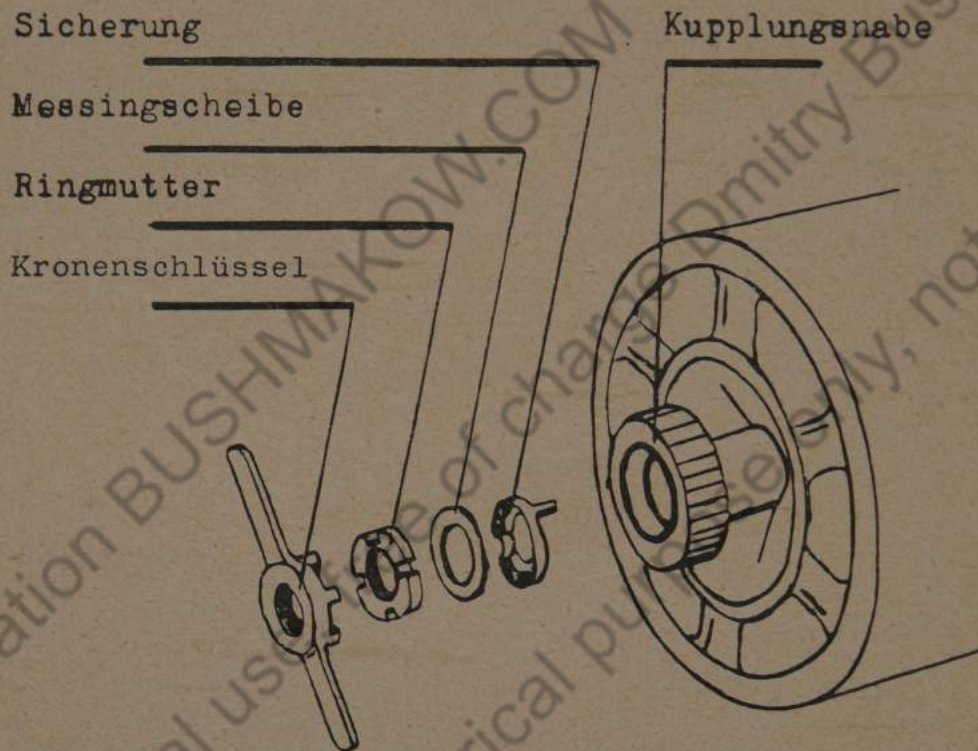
Entfernen der Ringmutter, Sicherung und Messingscheibe
